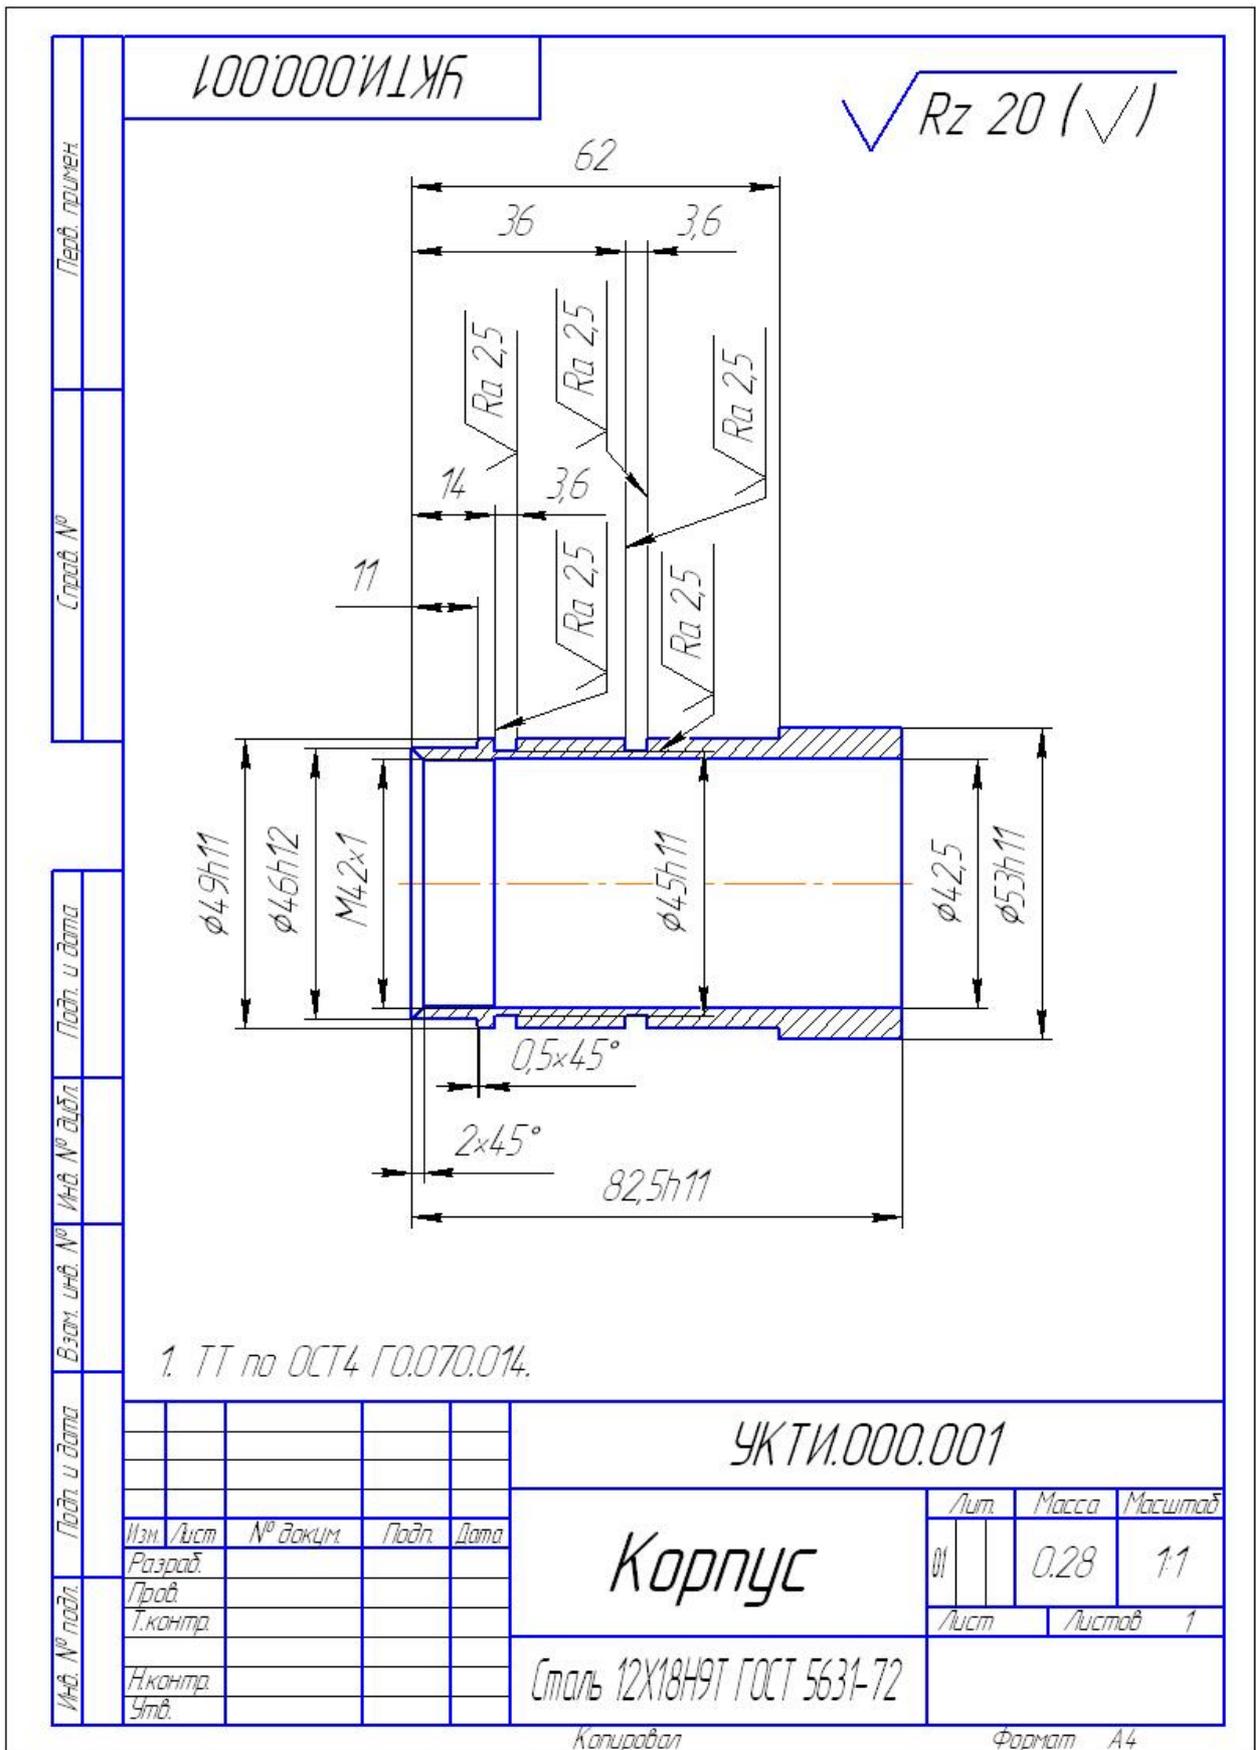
Чертеж детали УКТИ.000.001 Корпус
